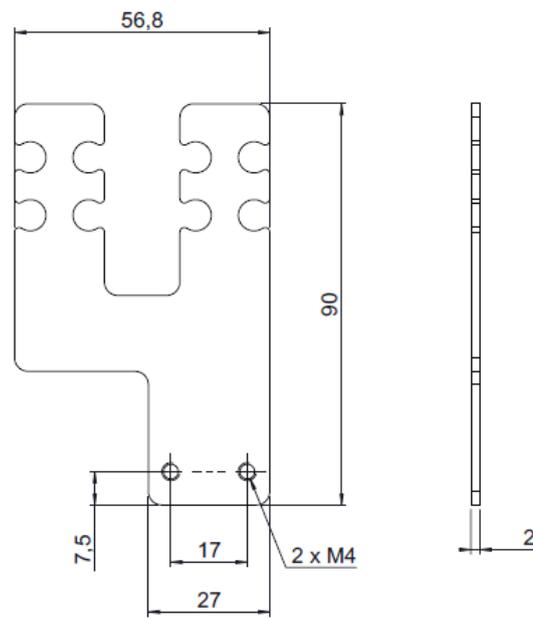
Mechanische Abmessungen Schirmblech
